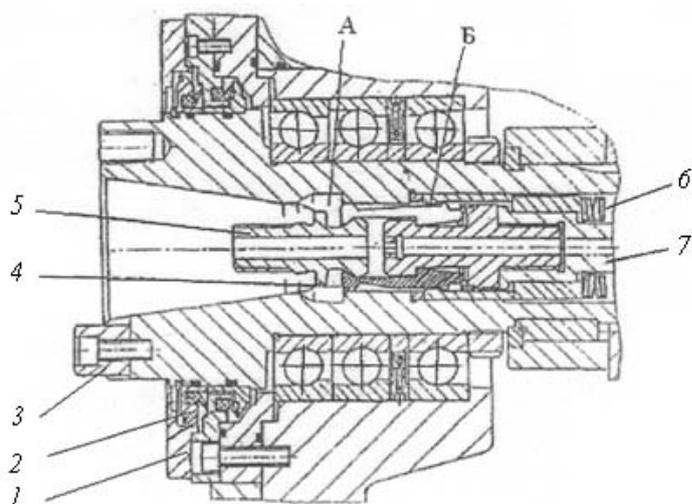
Шпиндельный узел многоцелевого фрезерно-сверлильно-расточного станка
